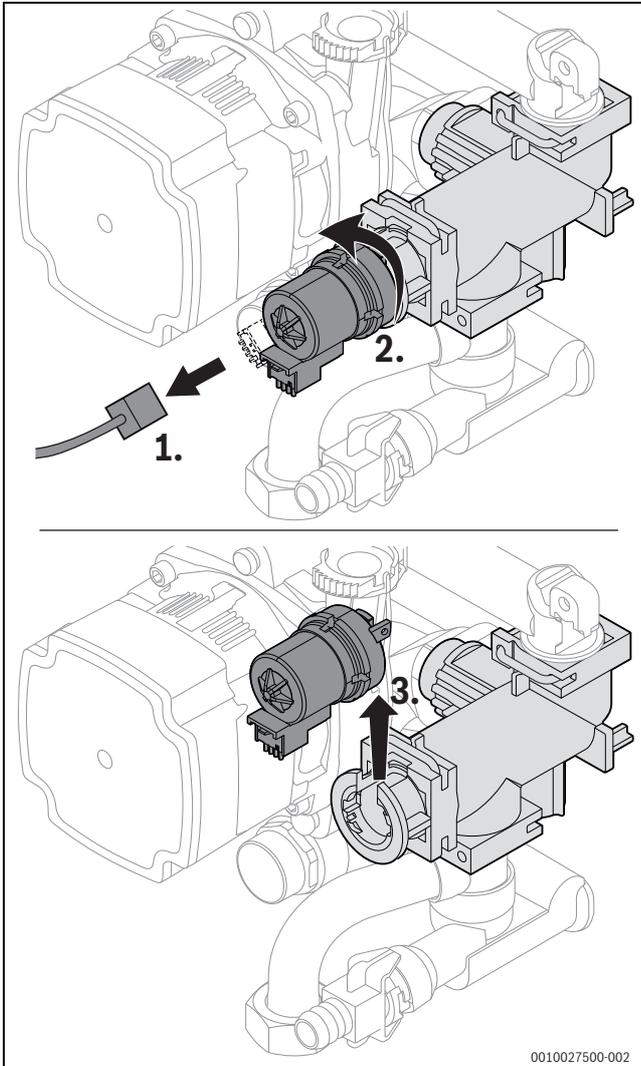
Motor am 3-Wege-Ventil ausbauen (Variante ohne Schrauben)
